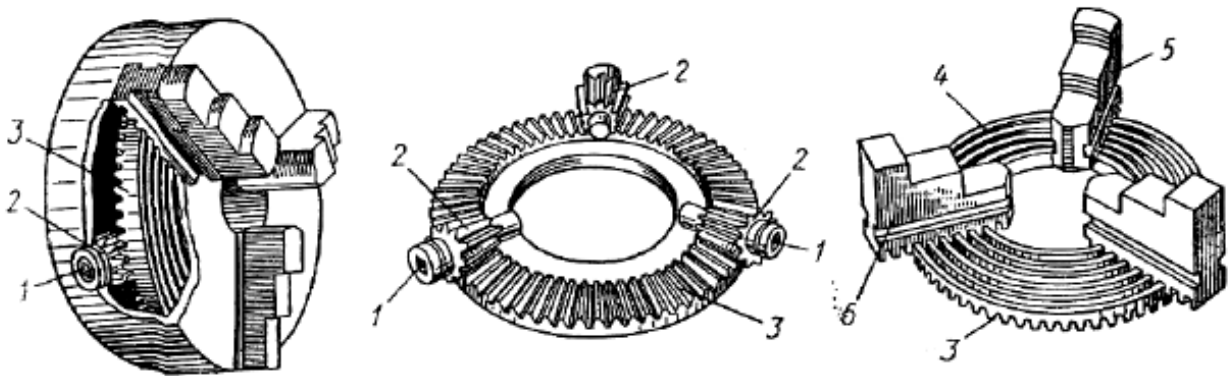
Самоцентруючий патрон: 1 – квадратні заглиблення; 2 – малі конічні колеса; 3 – велике конічне колесо; 4 – спіральна канавка; 5 – виступи кулачків; 6 - кулачки
